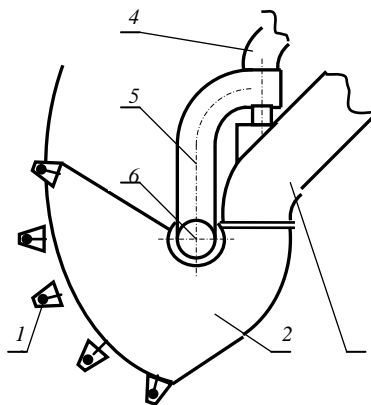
Поворотный рабочий орган с гидромеханическим разрыхлением грунта: 1 – зубья; 2 – поворотный экран; 3 – всасывающая труба; 4, 5 – трубопроводы; 6 – вал
